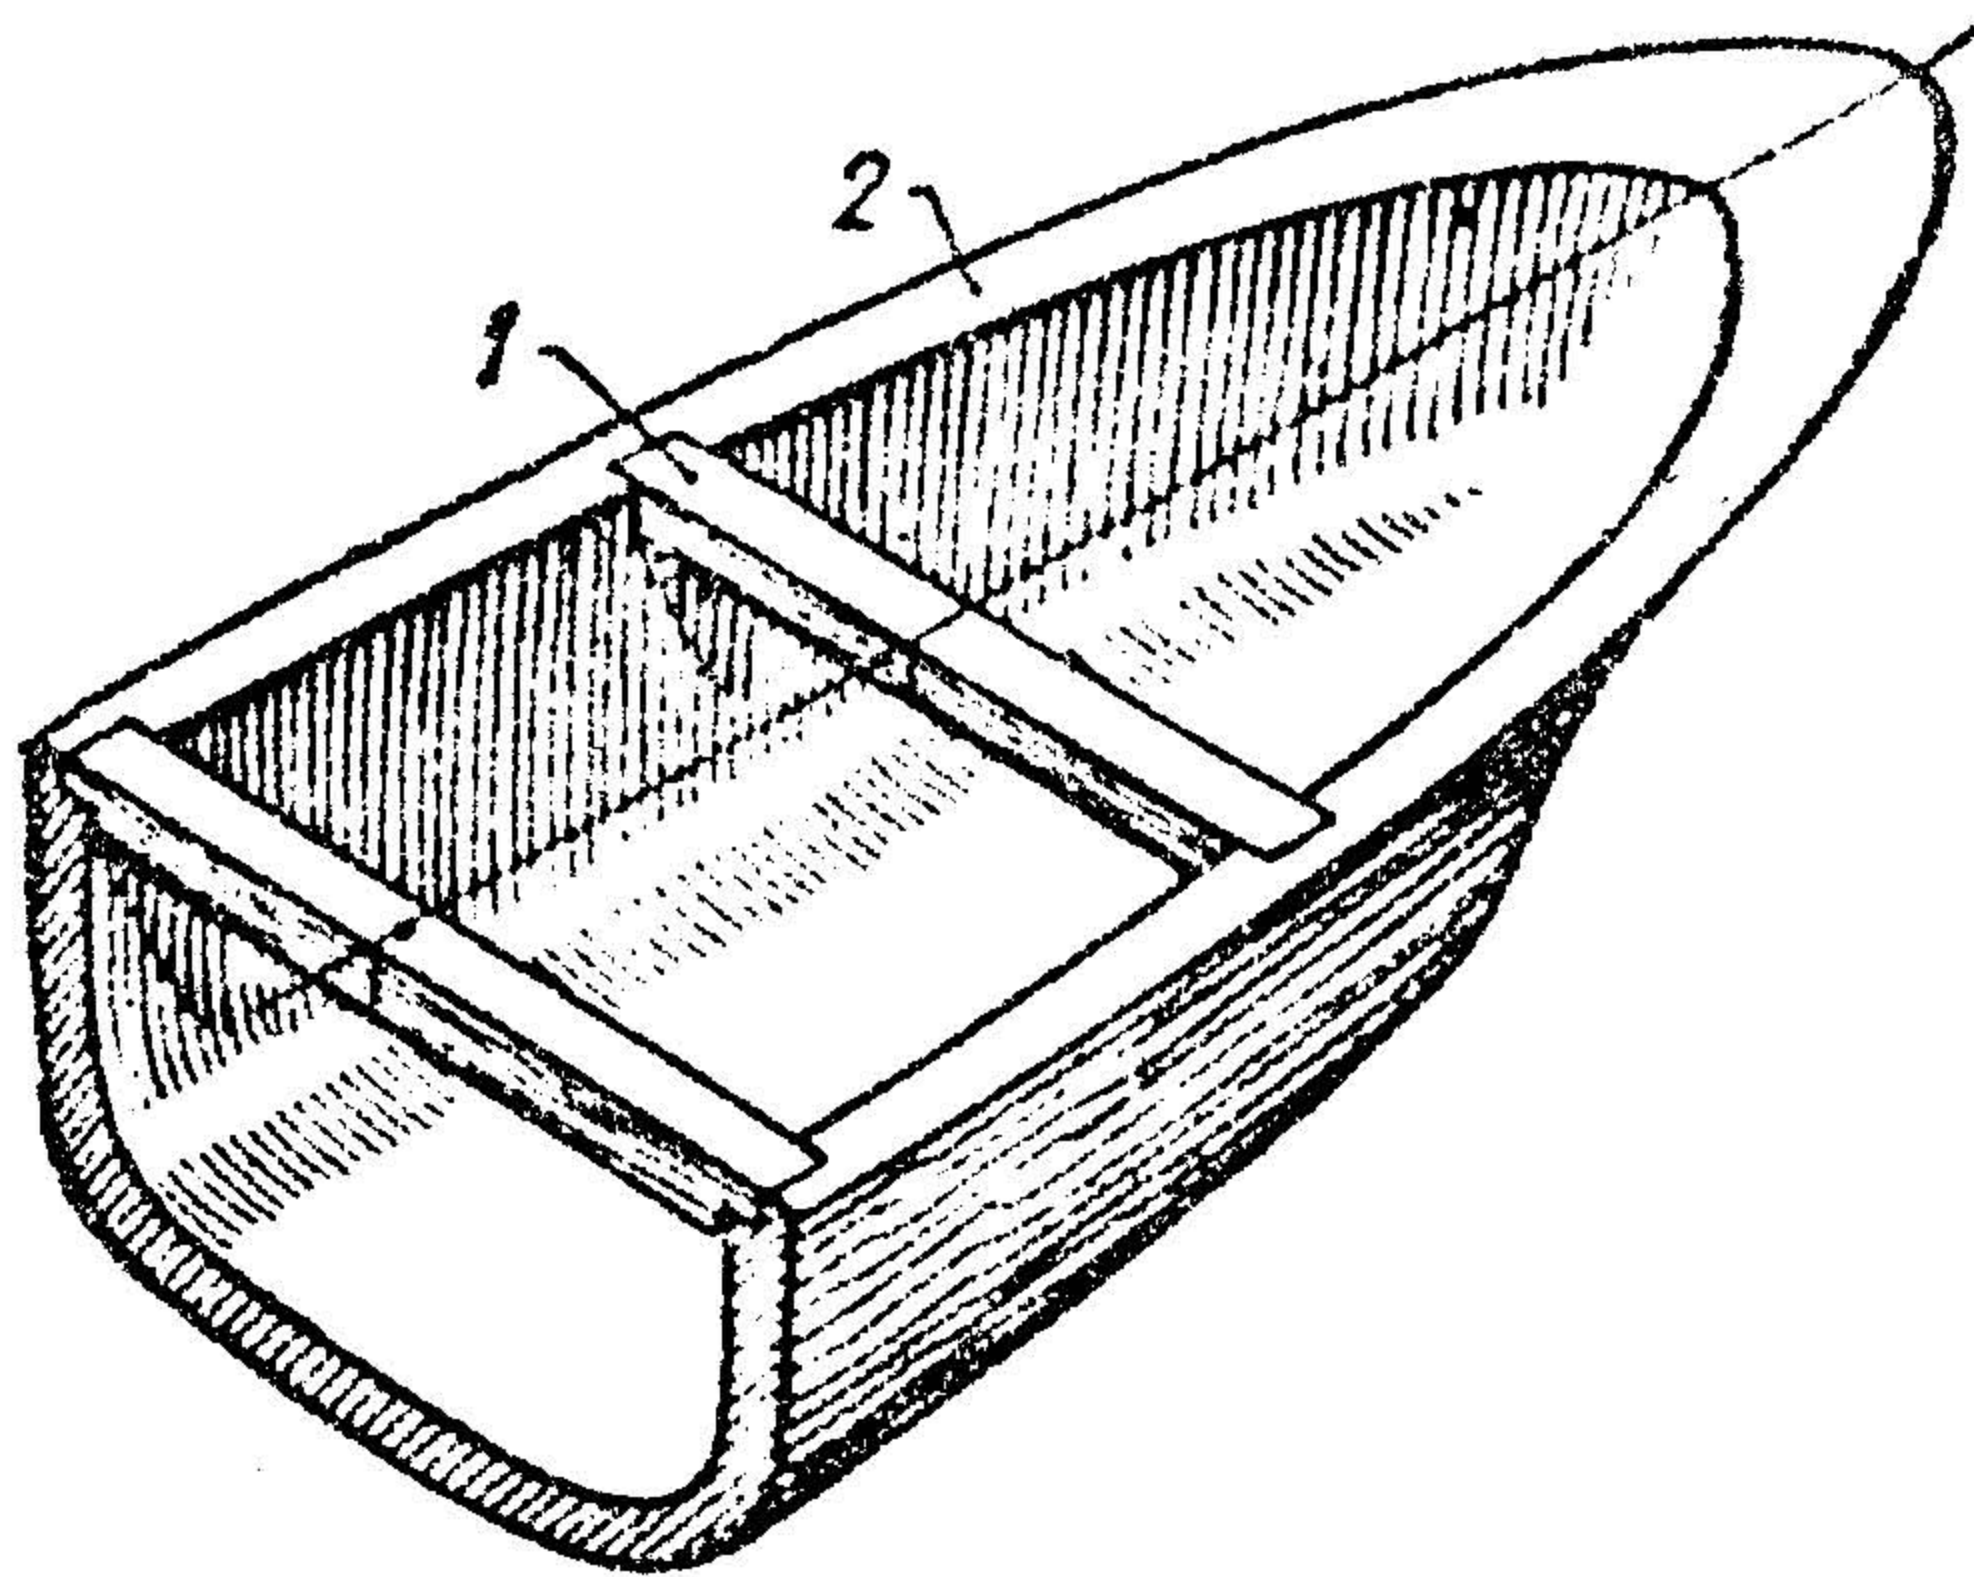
Крепление бимсов к корпусу: 1—бимс;
